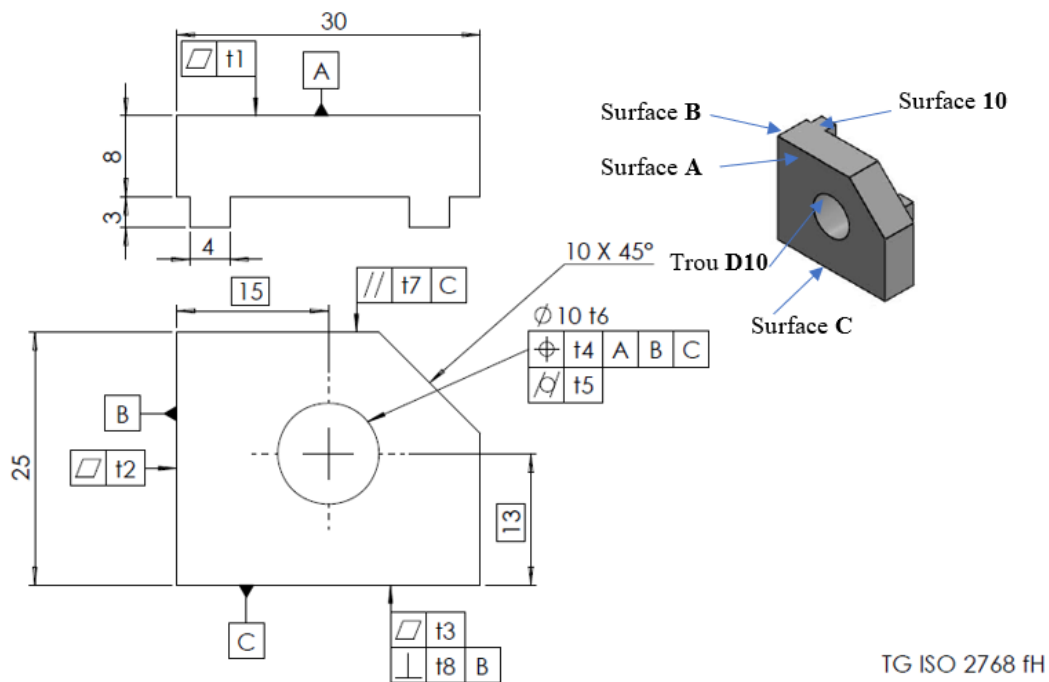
Vues de la pièce étudiée et repérage des surfaces.
